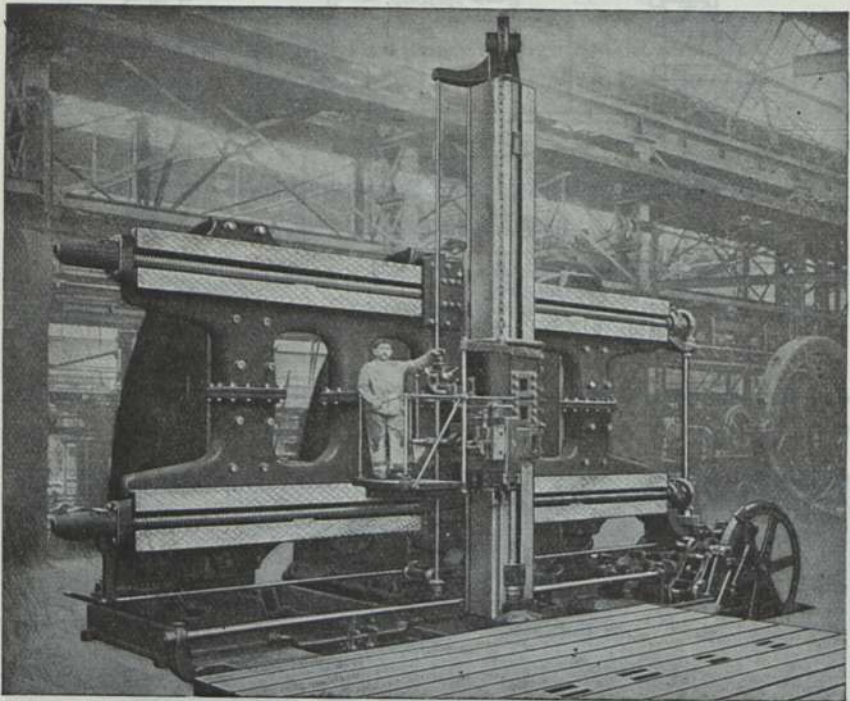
Senkrecht- und Wagerecht-Hobelmaschine der Kalker Maschinenfabrik, A. G., Köln-Kalk.
